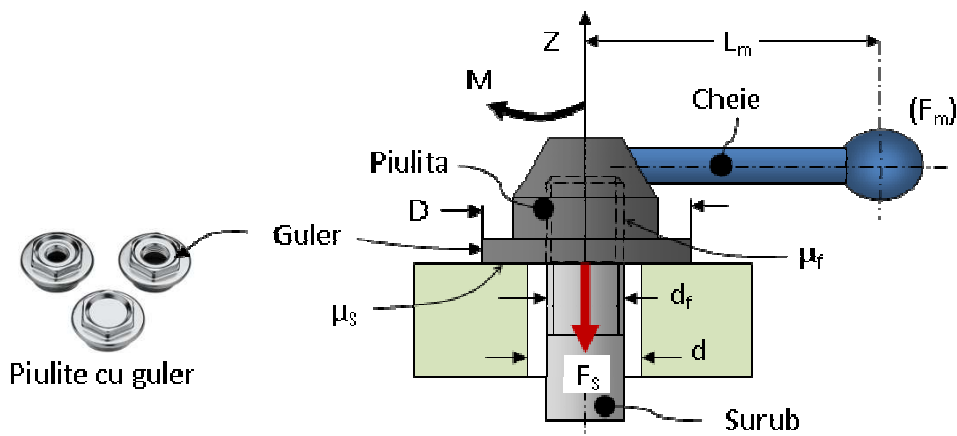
Mecanism de fixare cu piuliță cu guler plat
